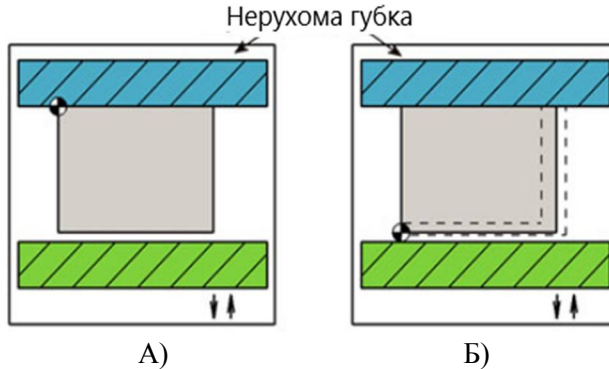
Знаходження нульової точки при встановленні заготовки в лещата
